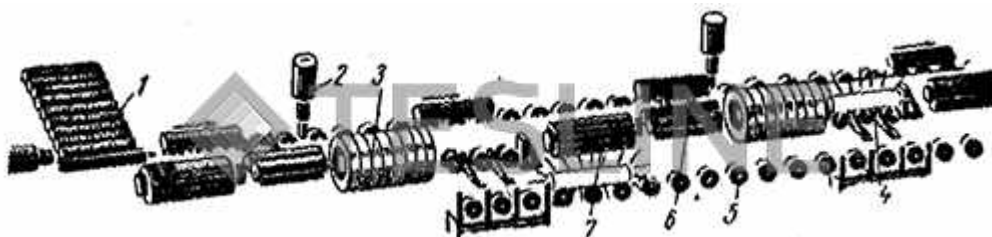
Схема нагревателя с двумя периодическими индукторами:
